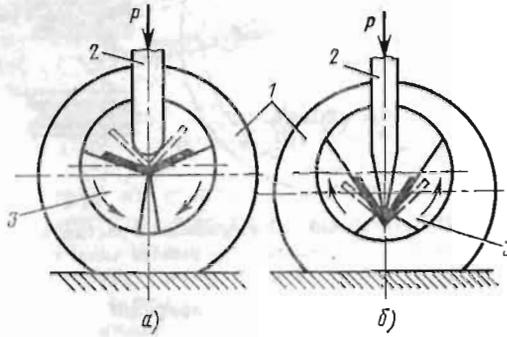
Схема малковочного штампа с поворотными сегментами:
